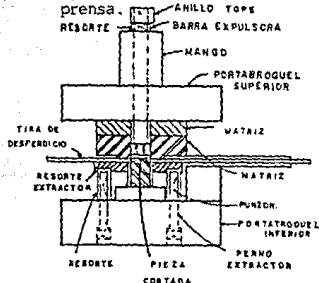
TROQUEL CORTADOR INVERTIDO
